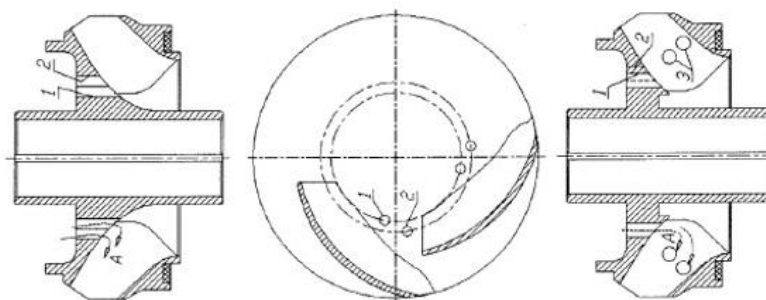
Рабочие колеса диспергатора типа AGH
